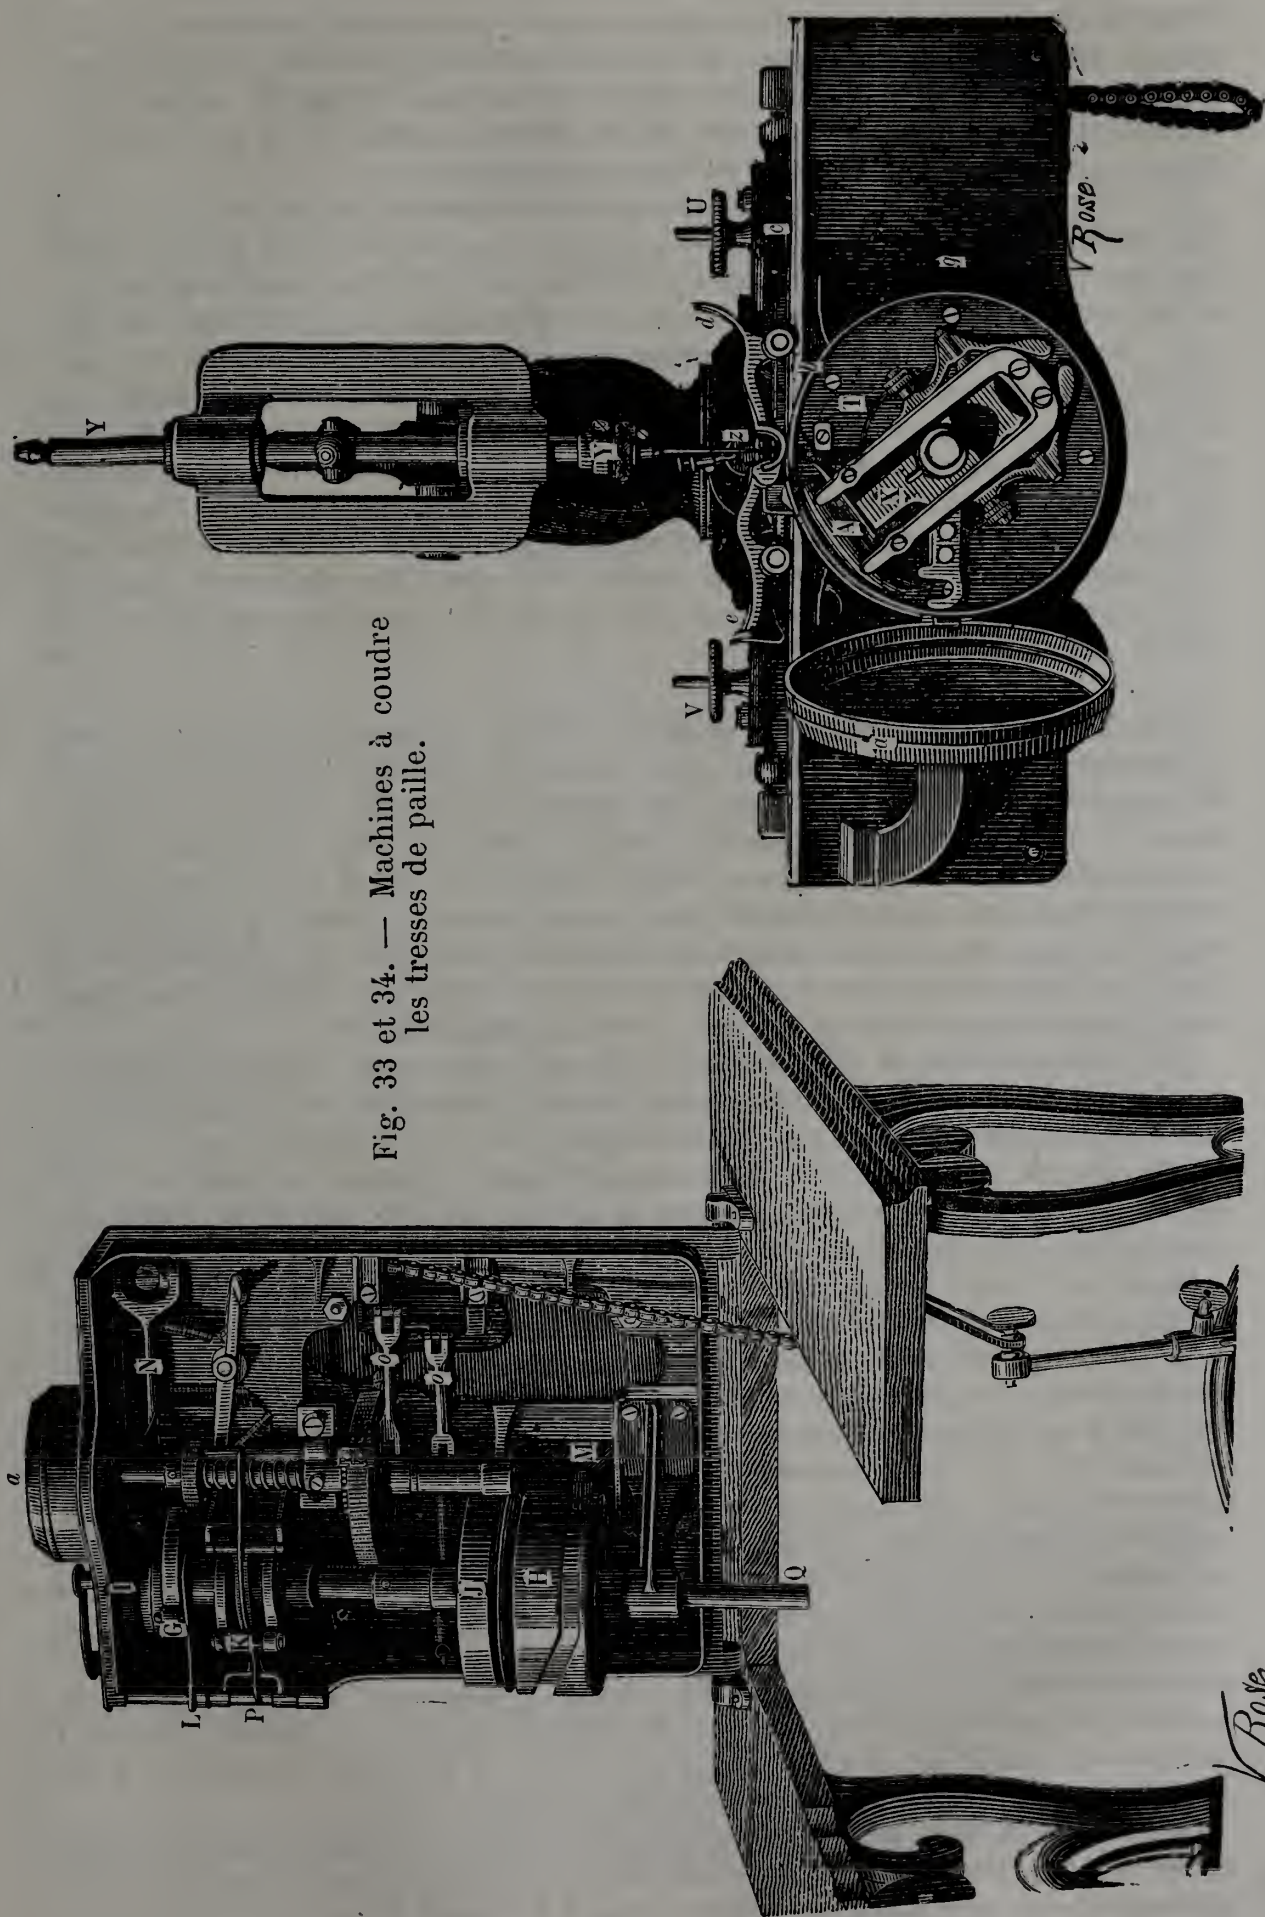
et 34. — Machines à coudre les tresses de paille.
